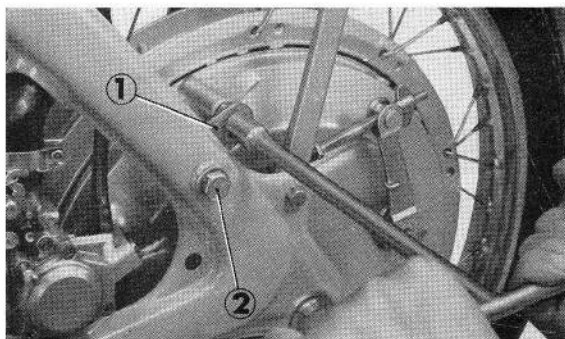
① bras de poussée arrière ② boulon de 8 mm
